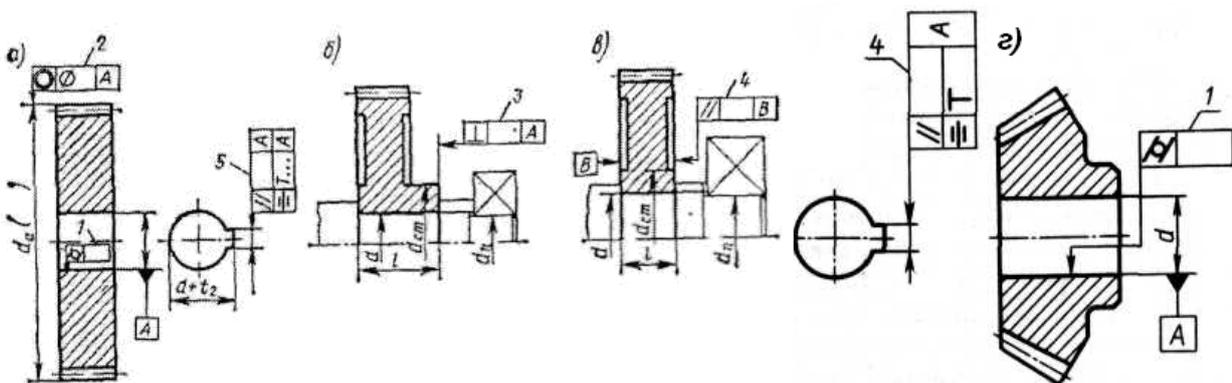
Допуски циліндричності посадочних поверхонь шестірні.
